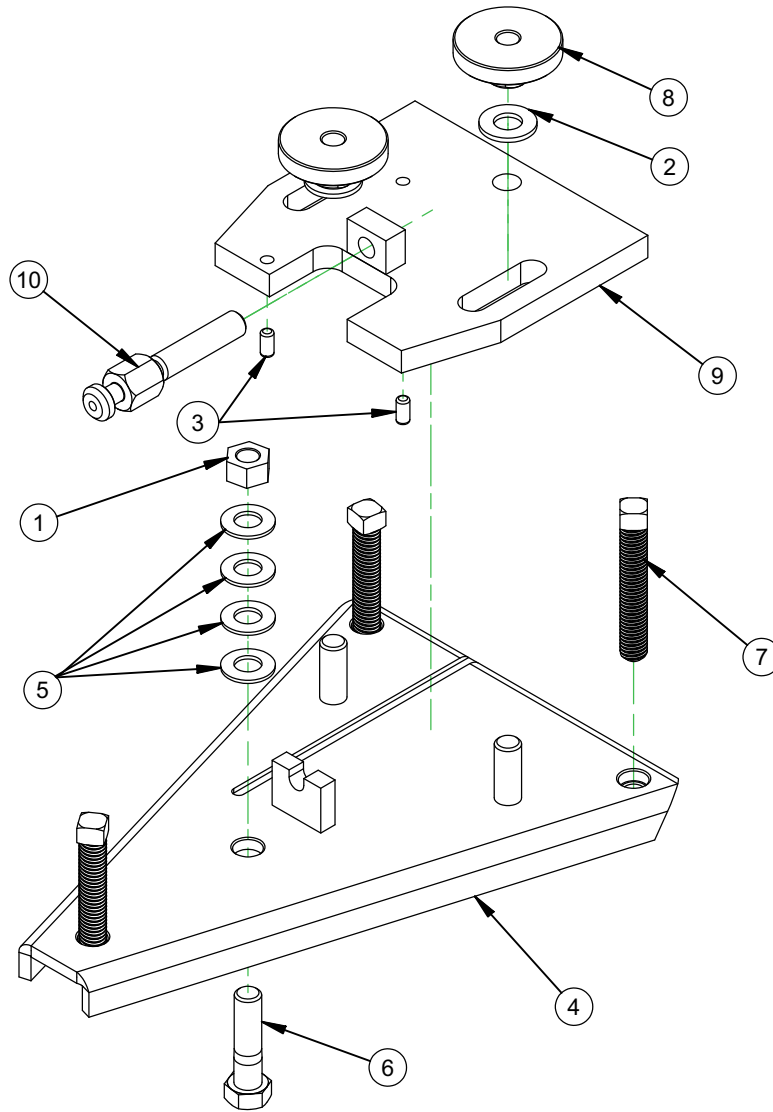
CONJUNTO DE CUBIERTA CON CONECTOR PLÁSTICO (N/P 68379)
